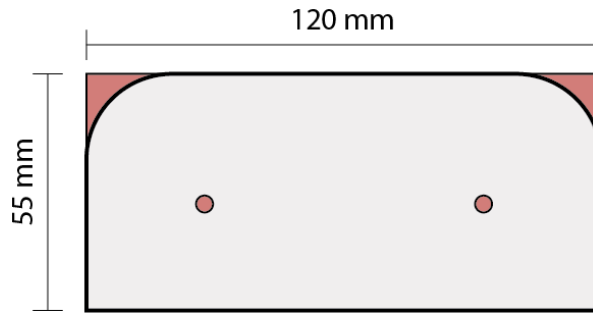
Dimensiones y desbaste del apoyo de presión para corte en plancha de grilon
